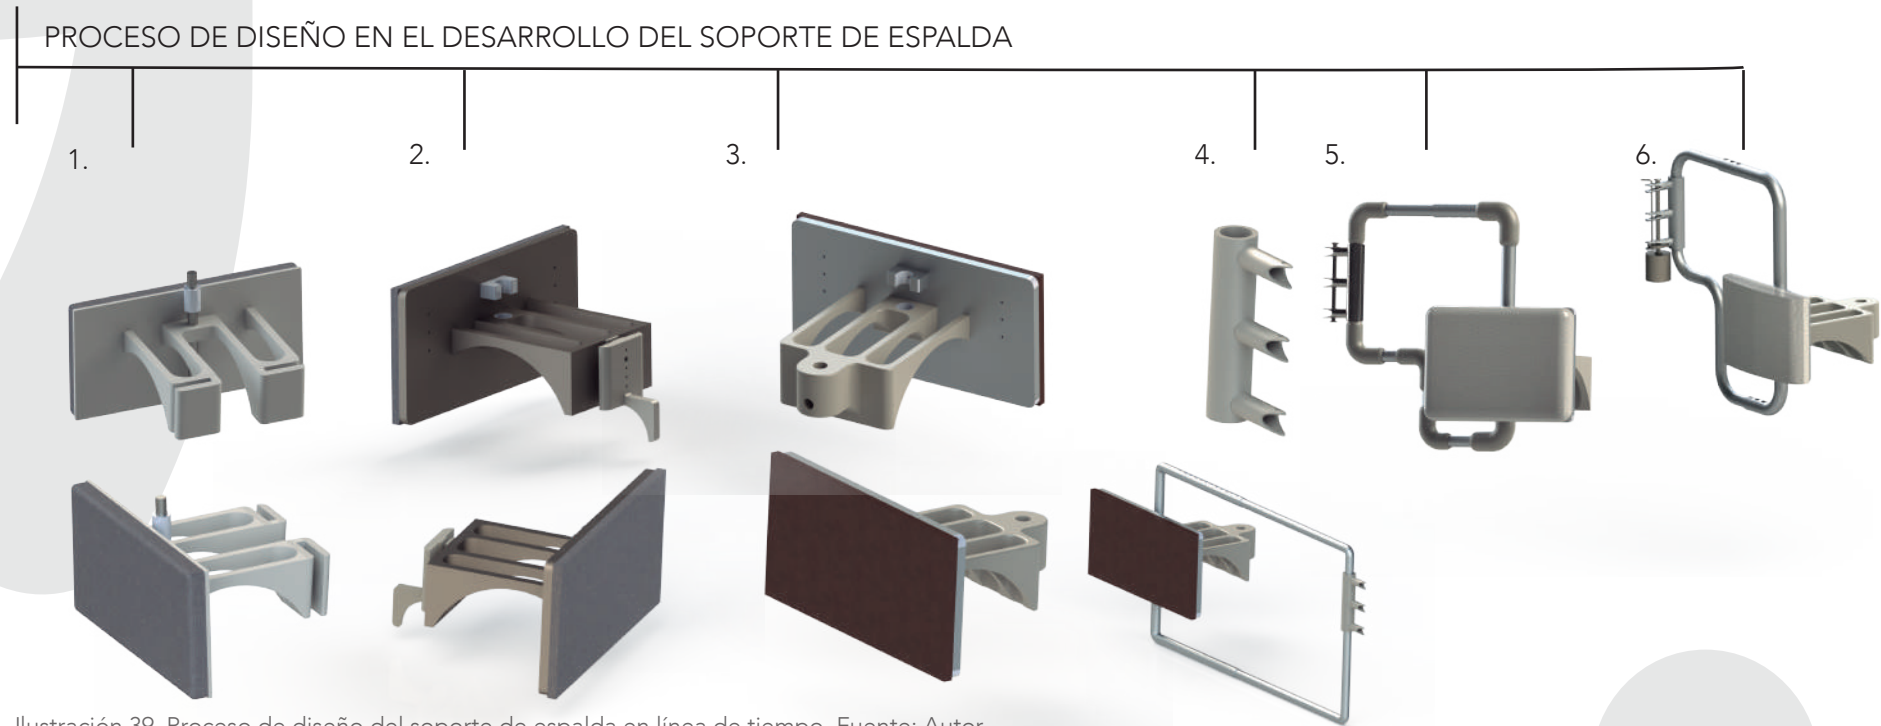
Proceso de diseño del soporte de espalda en línea de tiempo. Fuente: Autor.
